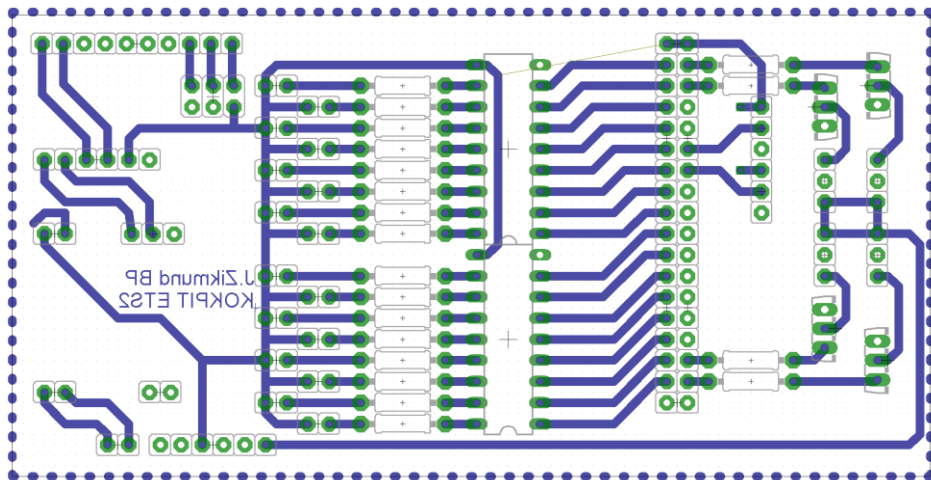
Zapojení D/A převodníku, zesilovače, reproduktoru a přípravy na budíky
